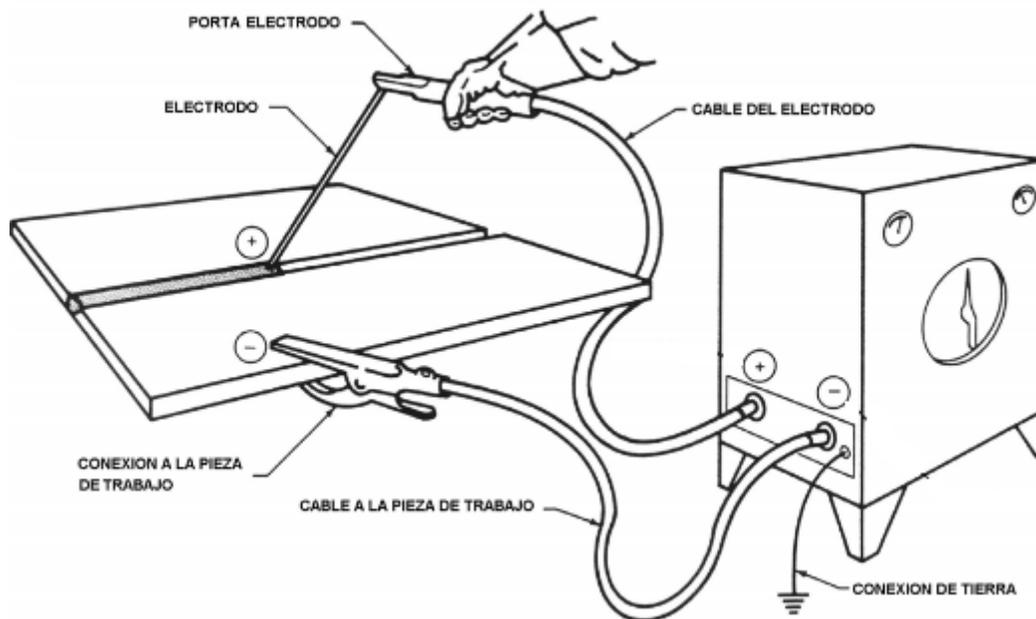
EQUIPO DE SOLDADURA SMAW.
